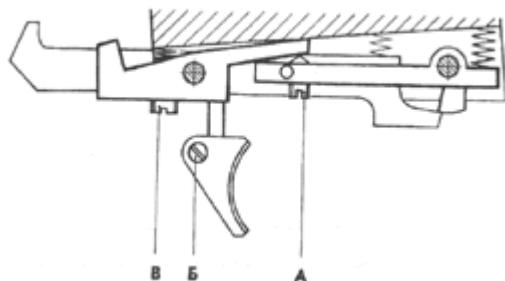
Схема спускового механизма винтовки ИЖ-61
